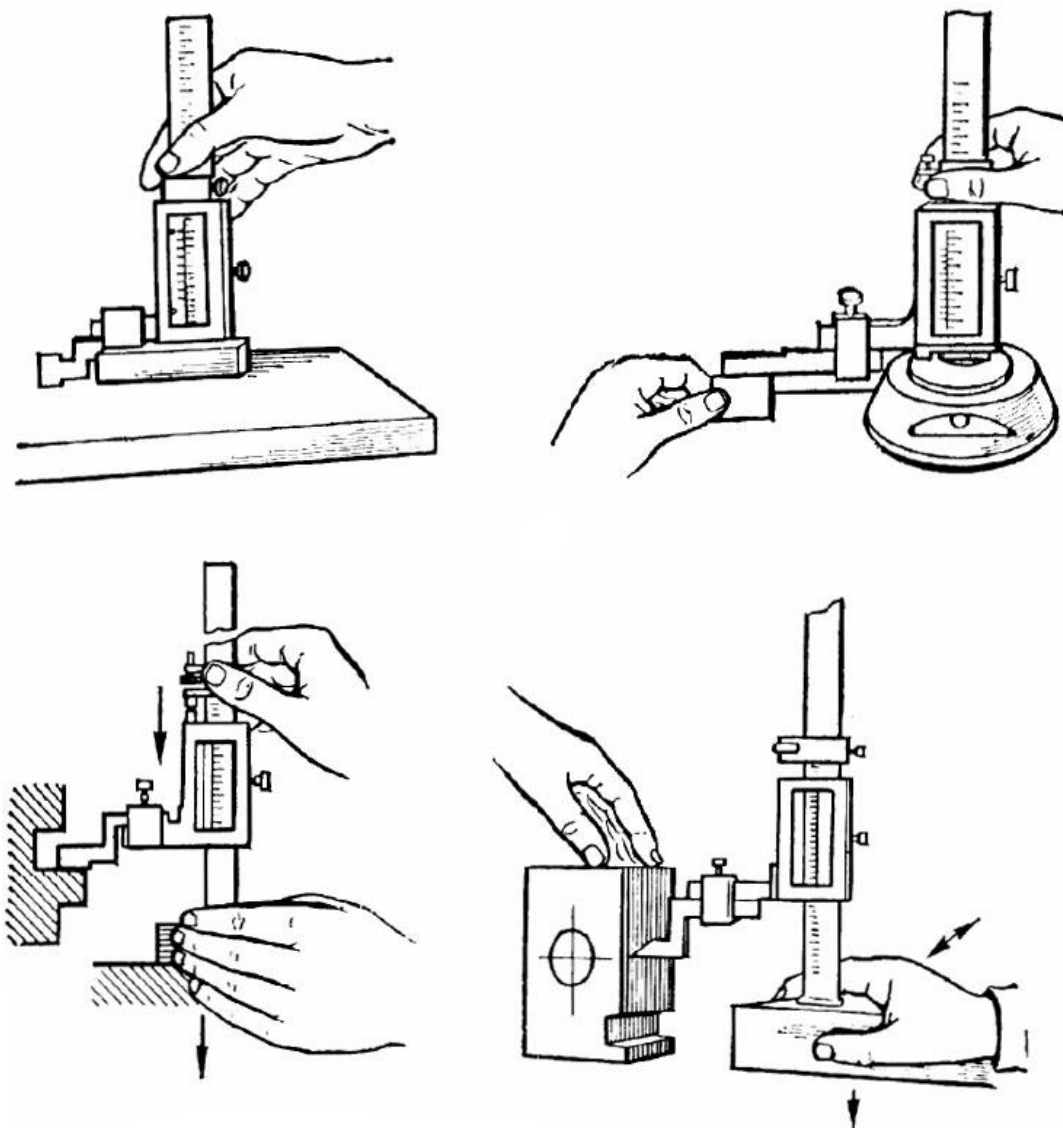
Перевірка нульового положення штангенрейсмаса, вимірювання та розмітка за допомогою штангенрейсмаса
